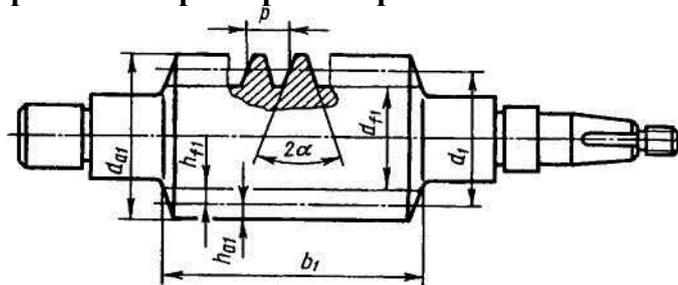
Основные размеры цилиндрического червяка делительный диаметр:
